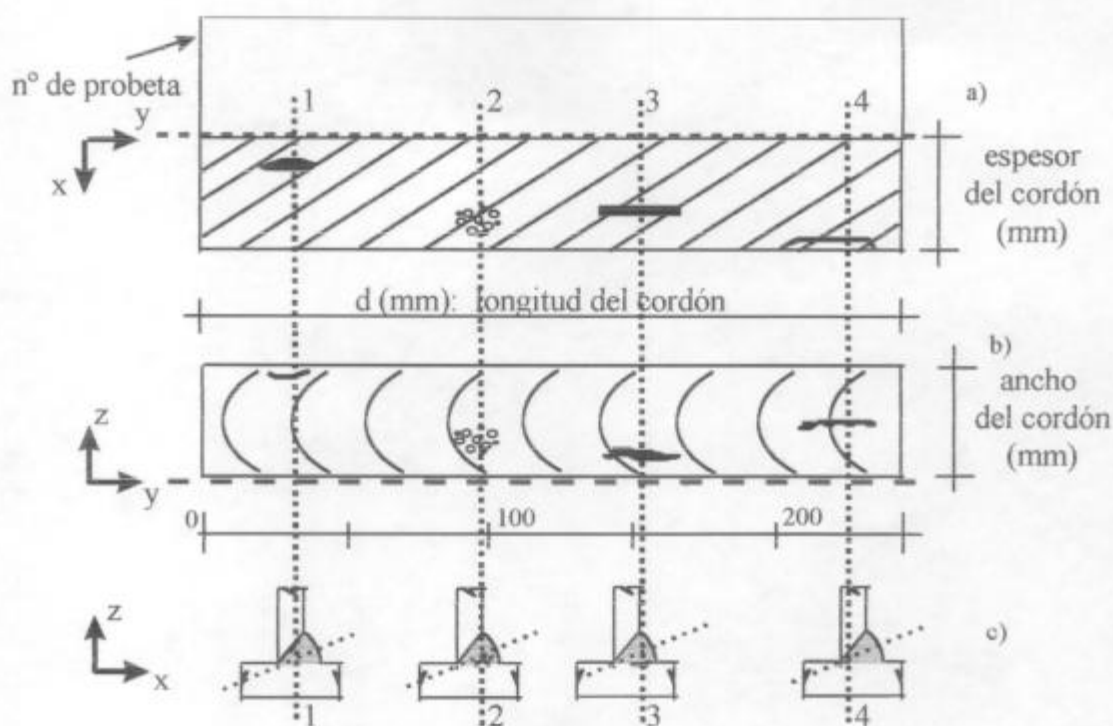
Registro de reflectores inducidos por soldadura
